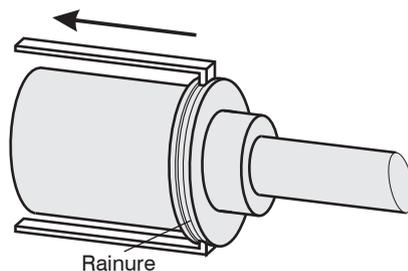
Démontage d'un induSENSOR, série EDS- ... -S
